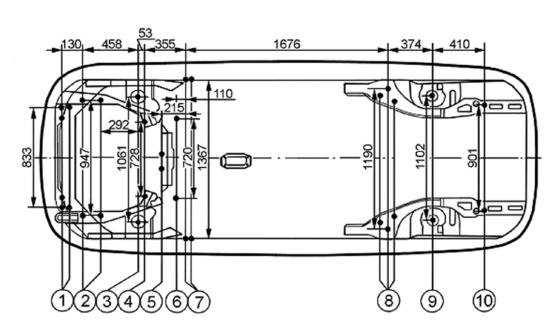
Точки крепления двигателя и подвесок на кузовах 1117; 1118; 1119, 2190, 2191, 2192, 2194
